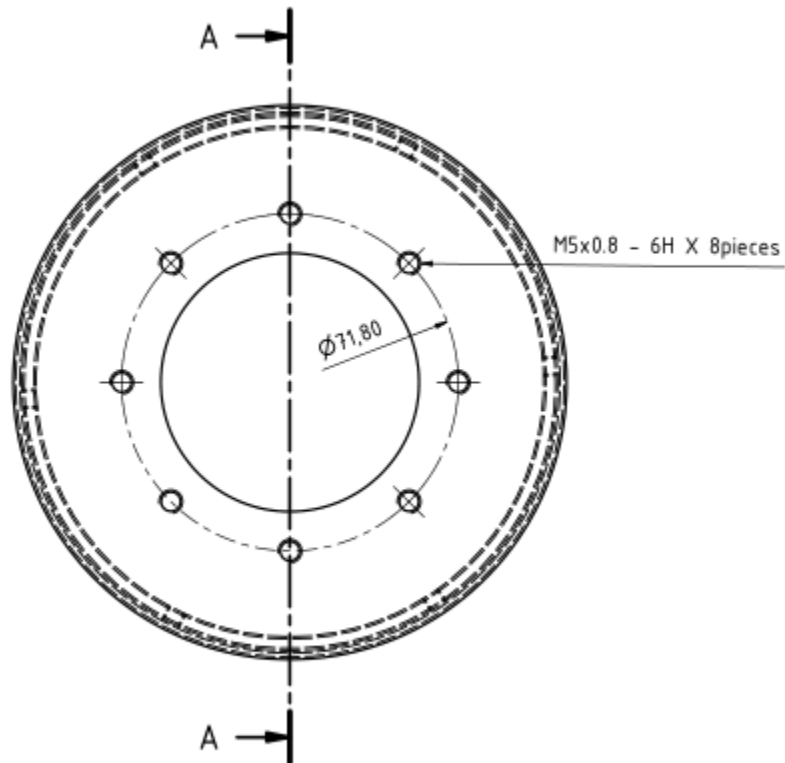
Vista frontal de la brida de montaje de la rueda.
